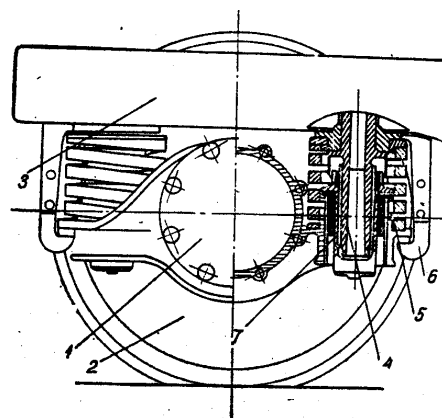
Локомотивна буса на плъзгаш лагер с фитилно мазане: 1-корпус; 2-тяло на плъзгащия лагер; 3-подложка; 4-маслен резервоар за горно мазане на лагера; 5-фитили за долно мазане на лагера; 6-притискаща пружина; 7-лагерна черупка; 8-уплътнение; 9-капак
